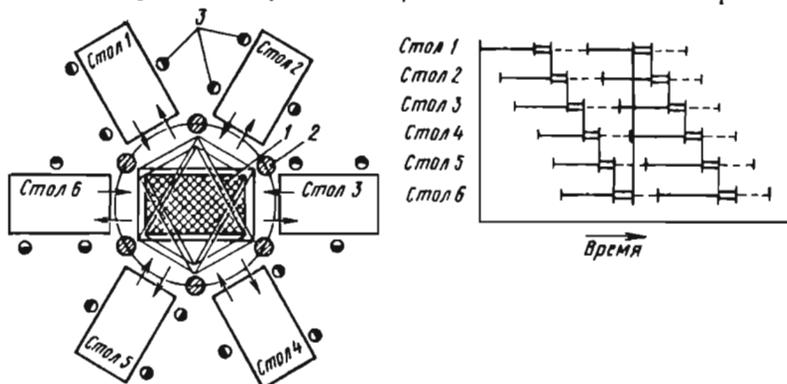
Схема и график работы гидравлического плунжерного прессы штамповки эластичной средой с шестью столами:
